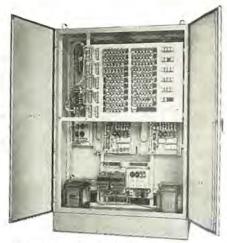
PK-80 形彫盤 ナライ 制御箱 Automatic copying controller for machine tools.
